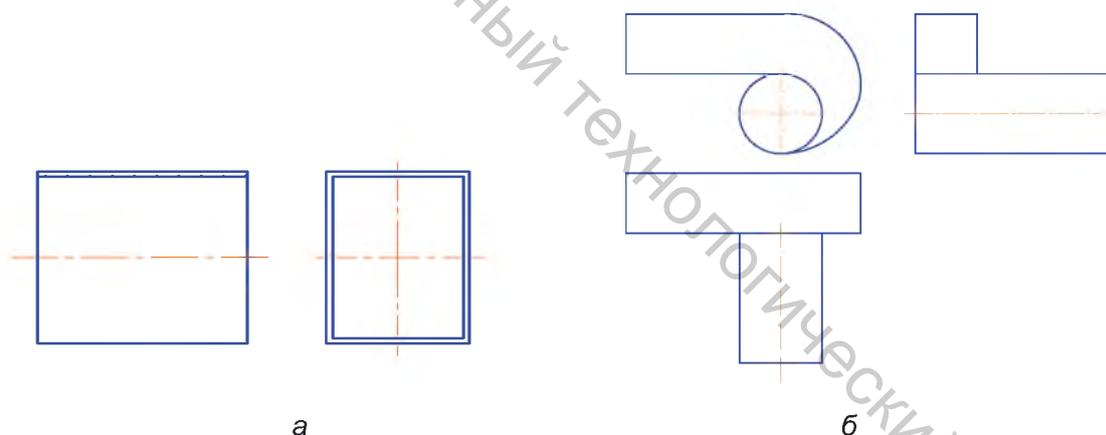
Конструкции сушильных камер: а – в виде короба, б – в виде вихревой трубы
